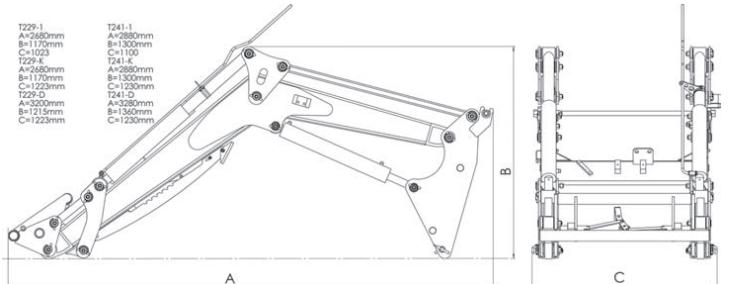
Размеры погрузчика, подготовленного для транспортировки как груз.
